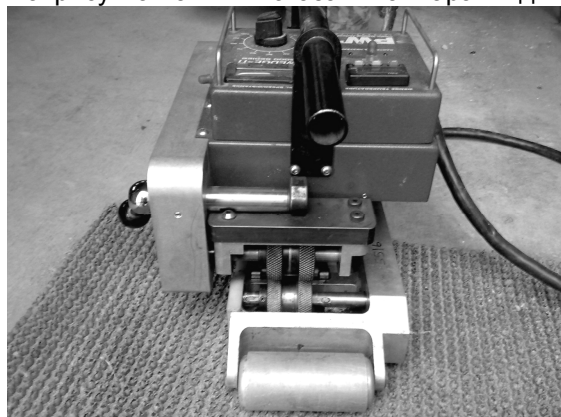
Аппарат для сварки геомембраны нагретым клином
